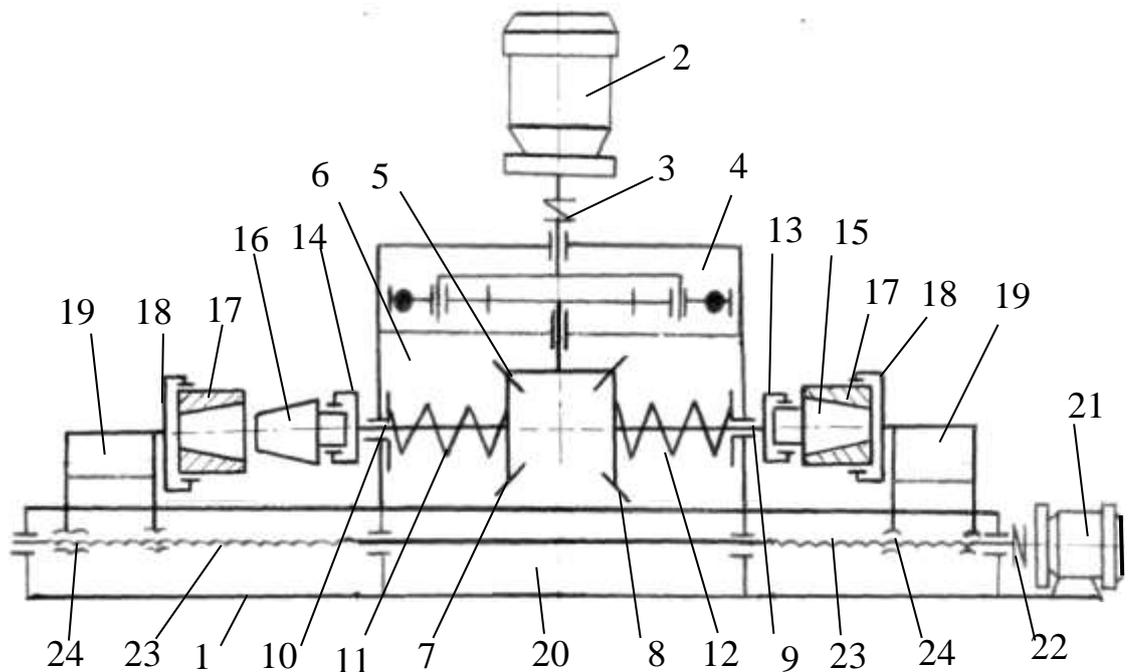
Кинематическая схема станка для притирки конических отверстий
